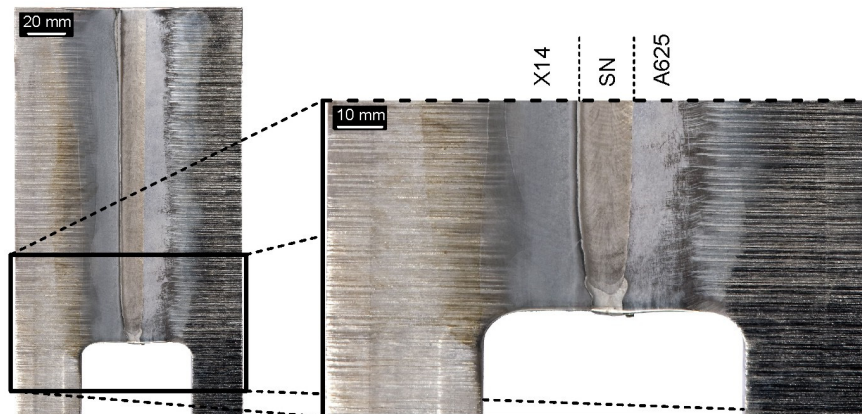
Aufbau der Rotorschweißverbindung, Makroaufnahme
